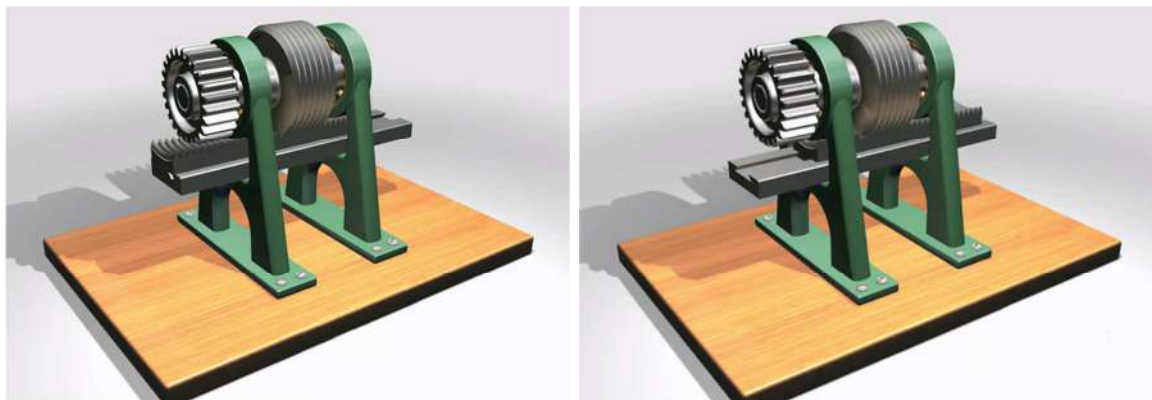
3D-модель черв'ячно-рейкової передачі (рейка рухома)
